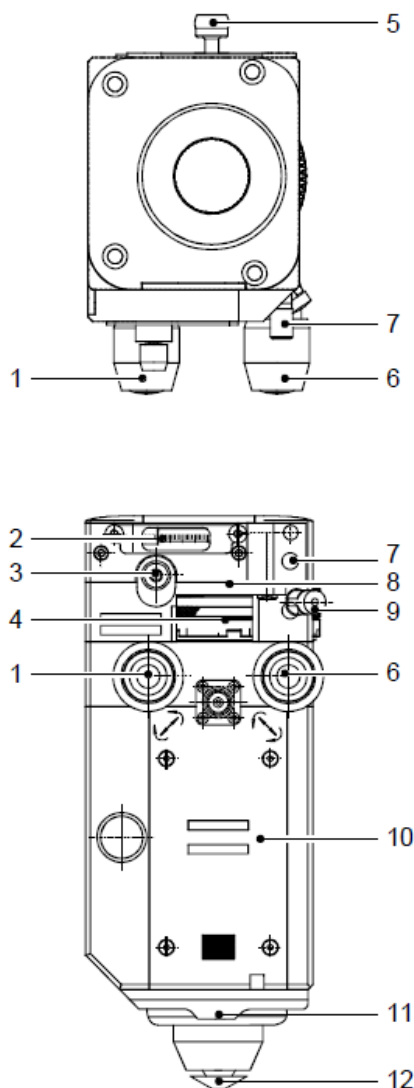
Vedení paprsku systémem TFL 4000 [14]
